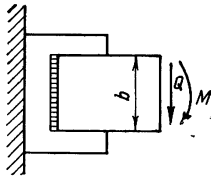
Нагруженные соединения с лобовым швом моментом и поперечной силой
